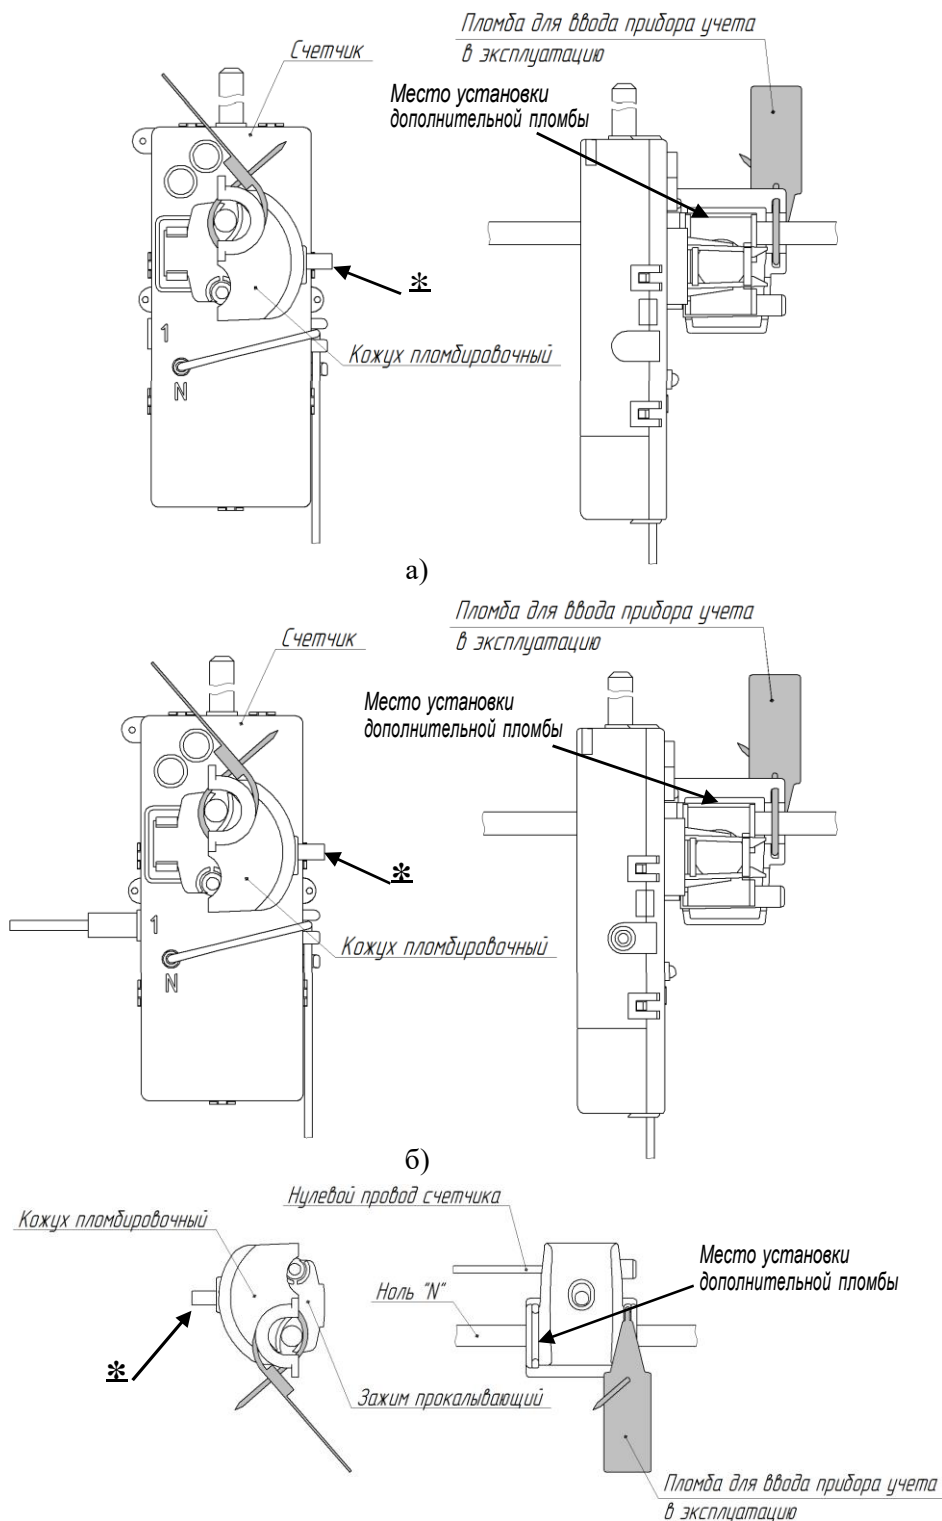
Установка кожуха пломбировочного на счетчики в корпусе Тип I
